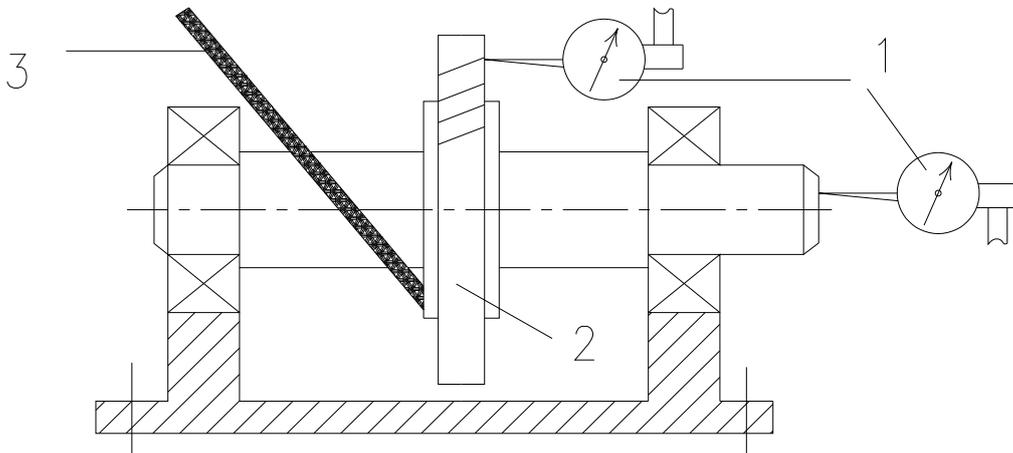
Проверка осевой игры в подшипнике качения с помощью индикатора: 1 – индикатор; 2 – зубчатое колесо; 3 – щуп
